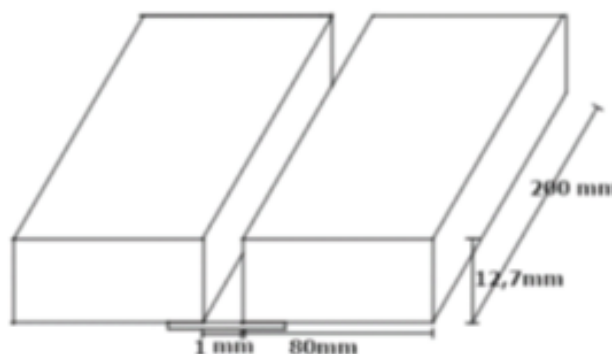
Geometria da junta de topo utilizada para soldagem com diferentes tipos de *backing*.
